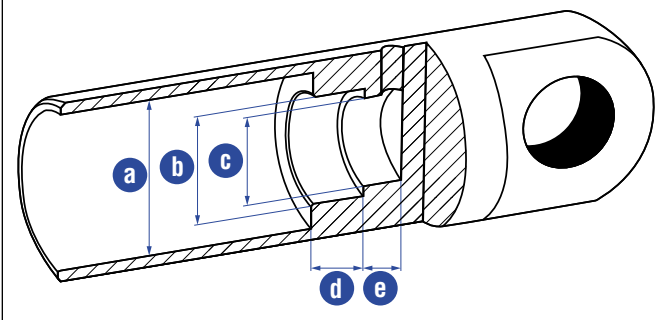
Bauraum Mindestanforderungen für Zylinder
